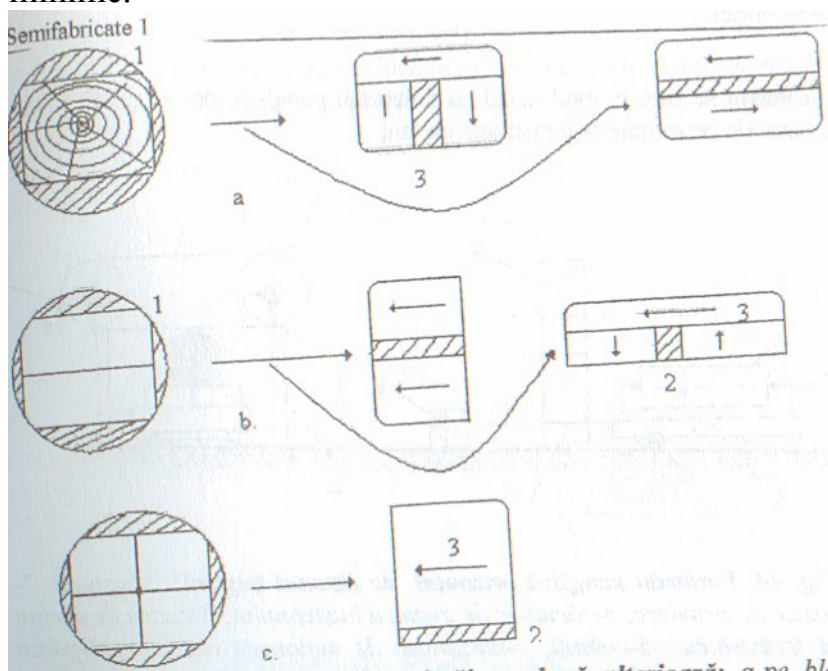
Modalități de fasonare și tăiere plană ulterioară: a-pe bloc întreg; b-pe jumătăți; c-pe sferturi; 1-margine de fasonare; 2-rest cuțit; 3-direcția de tăiere.
